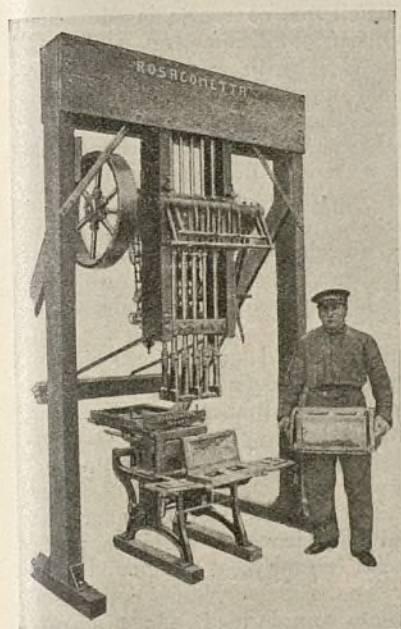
Disposición general de la prensa automática "Rosacometta"
